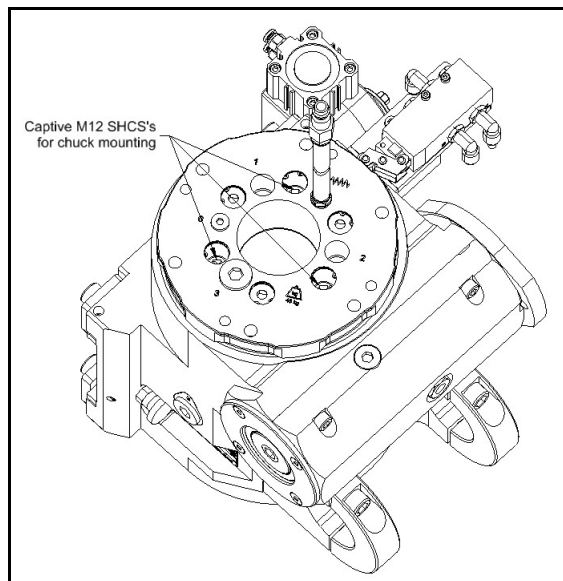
FIXATION DE L'ENSEMBLE DE MONTAGE DE AU BLOC PRINCIPAL
